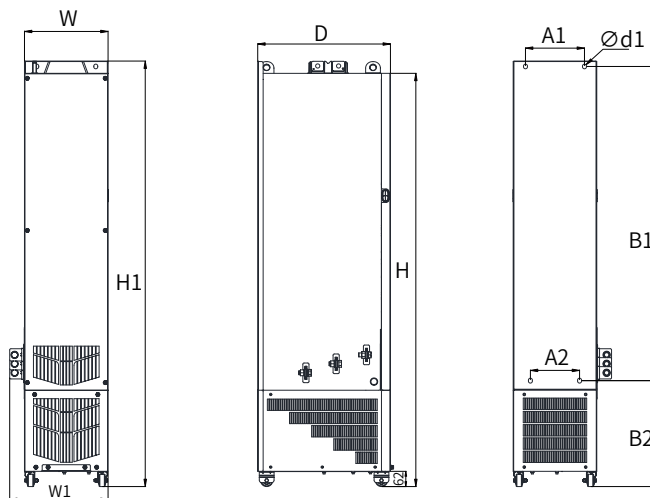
Габаритные и монтажные размеры конструкций Т10 - Т12 (с основанием под реактор)
